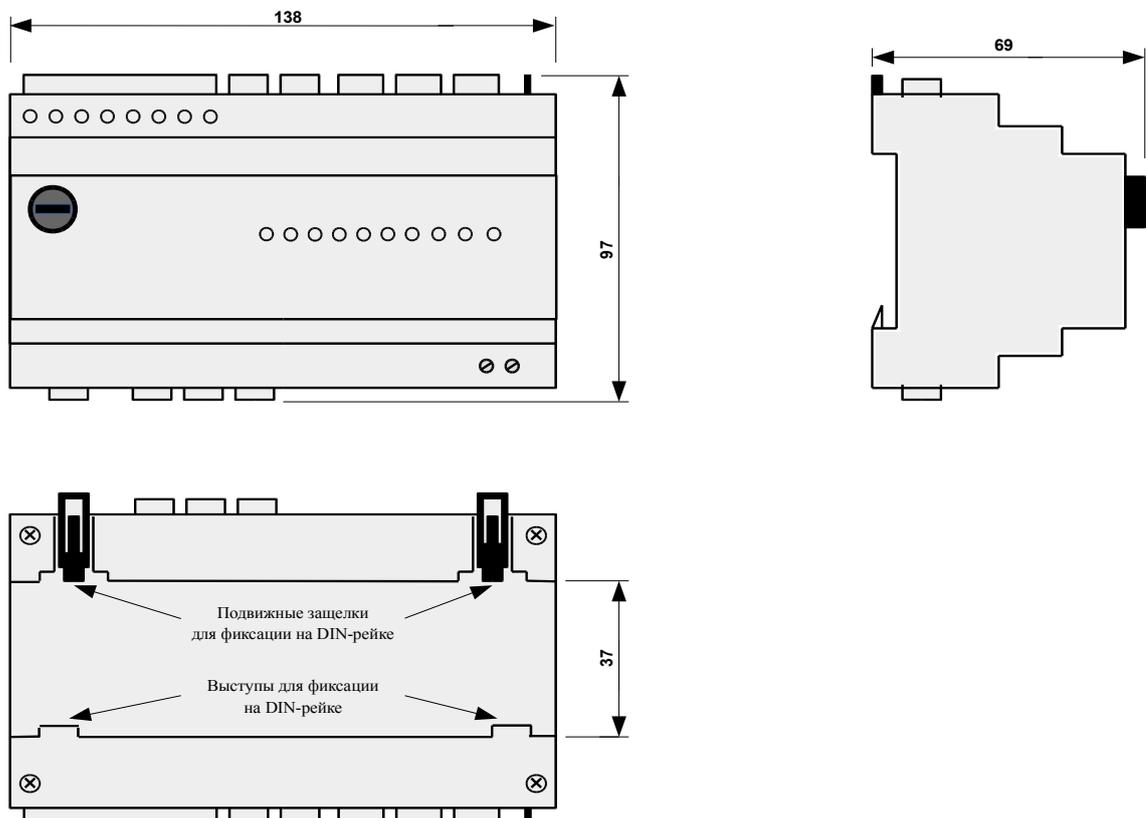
Габаритные размеры и крепление на DIN-рейке.
